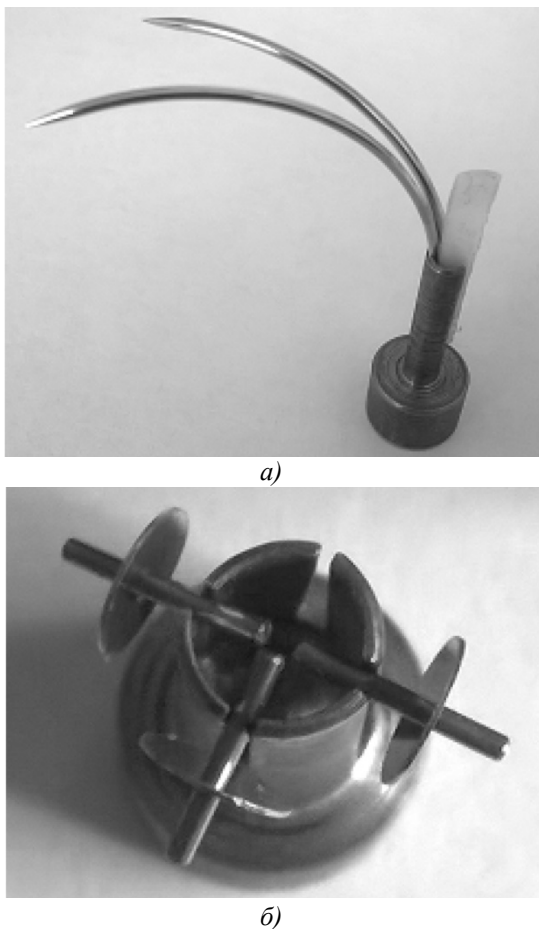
Примеры оснастки для групповой обработки мелкоразмерных заготовок:
